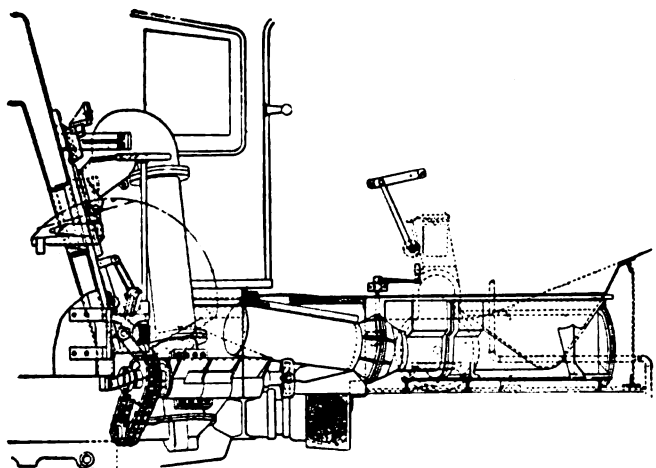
Caricatore meccanico del carbone sulle locomotive sistema Hanna.
